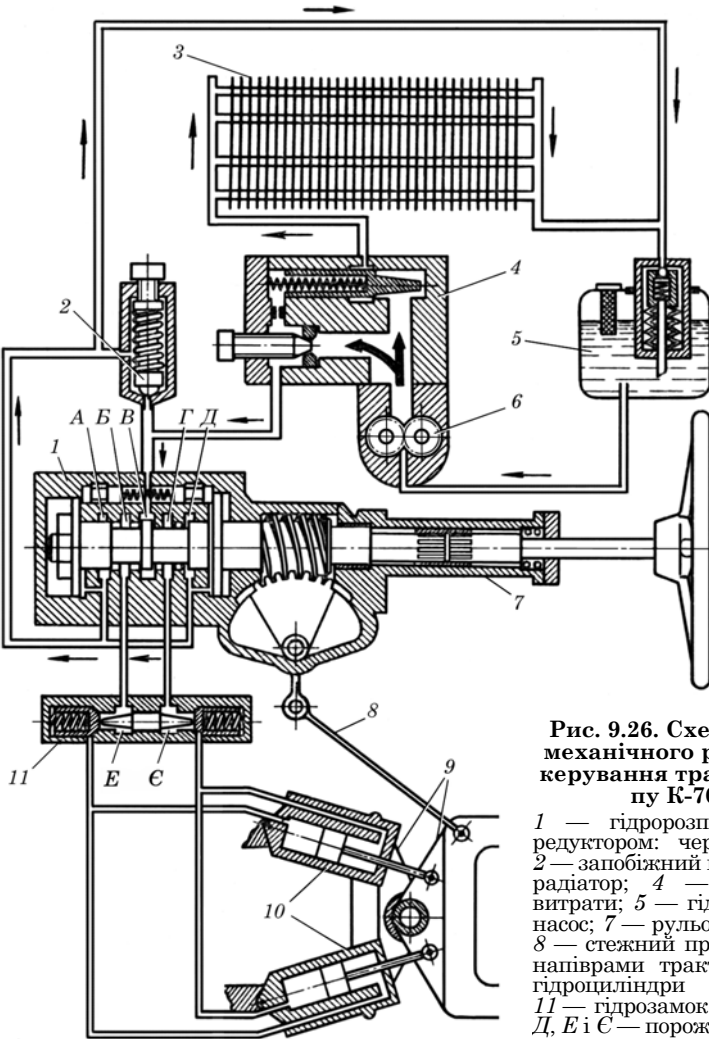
Схема гідромеханічного рульового керування трактора типу К-701:
